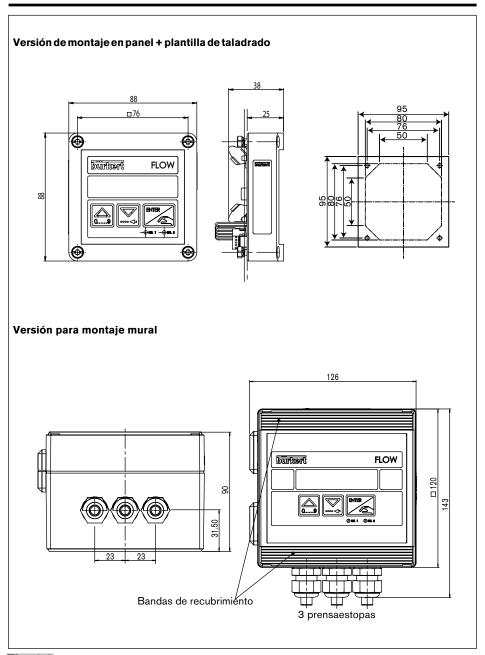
Dimensiones del caudalímetro 8025 independiente
